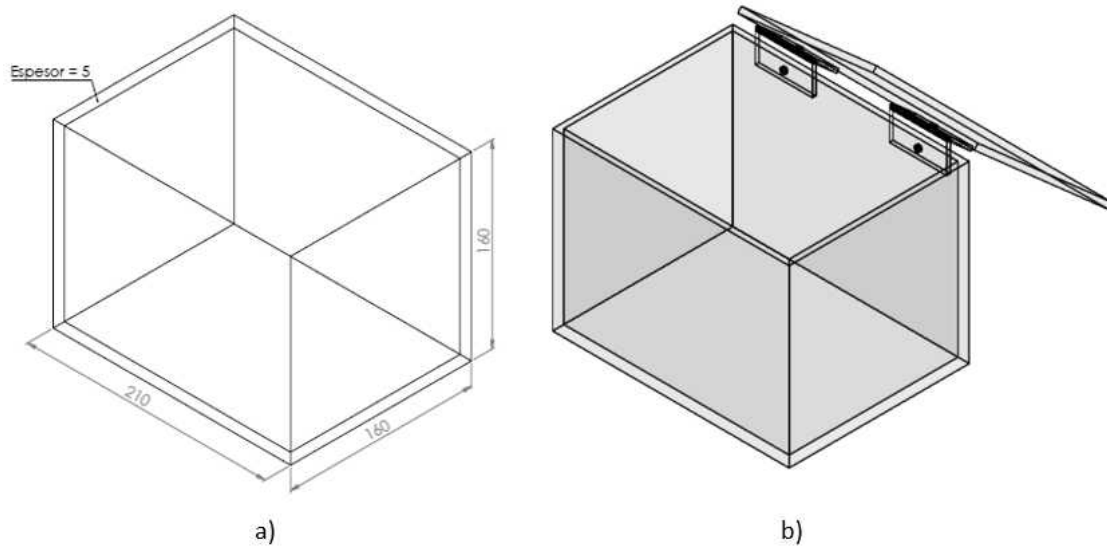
1.- a) Dimensiones generales de la cámara para el control de parámetros, b) vista isométrica del aspecto final de la caja de acrílico.
